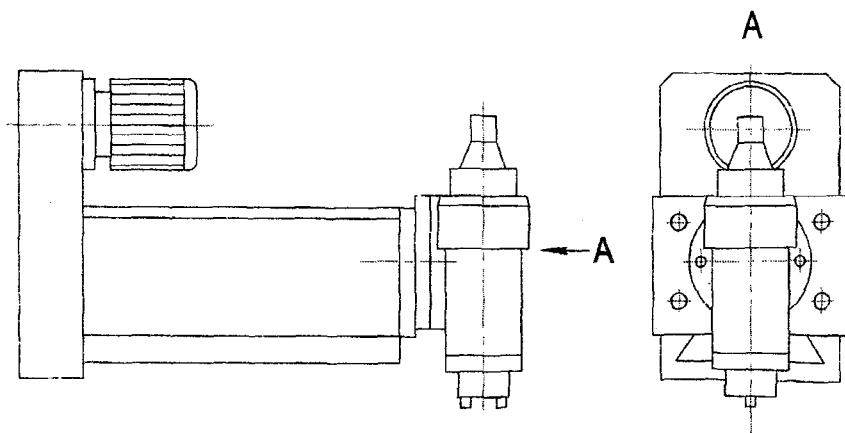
Компоновка шпиндельной бабки широкоуниверсально-фрезерного инструментального станка
